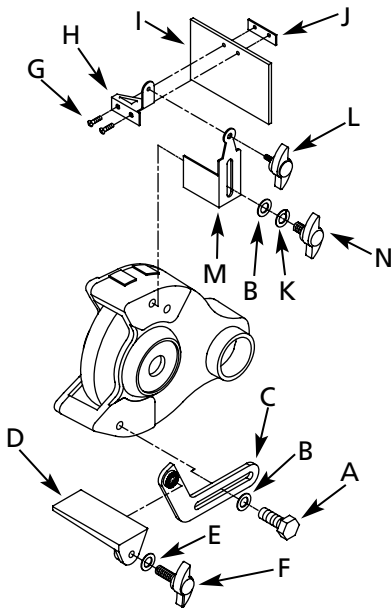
Soporte de la Herramienta Izquierdo y Conjunto de la Protección de Ojos
